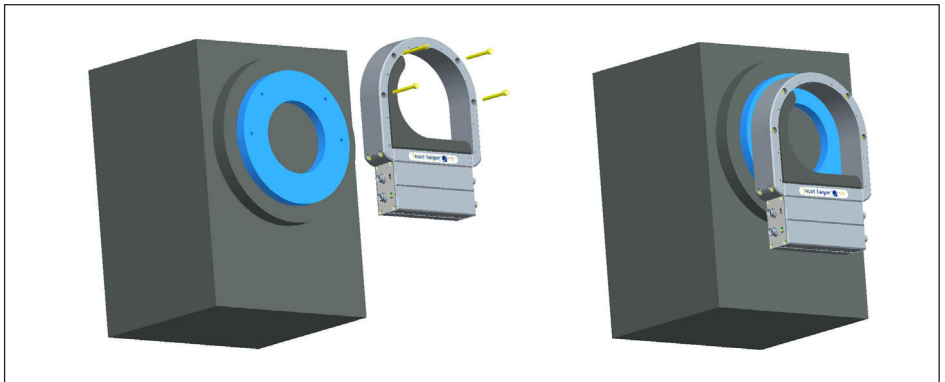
Montage stirnseitig am kundenseitigen Motorschild
